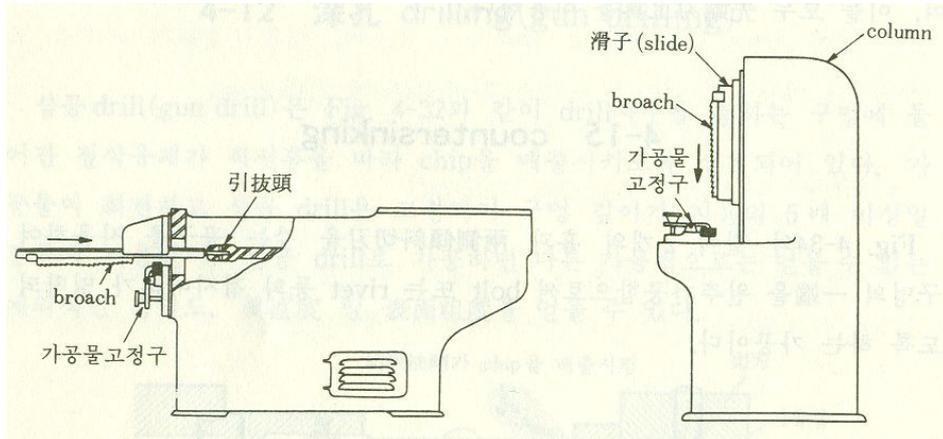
수평식(좌) 과 수직식(우) broaching machine
